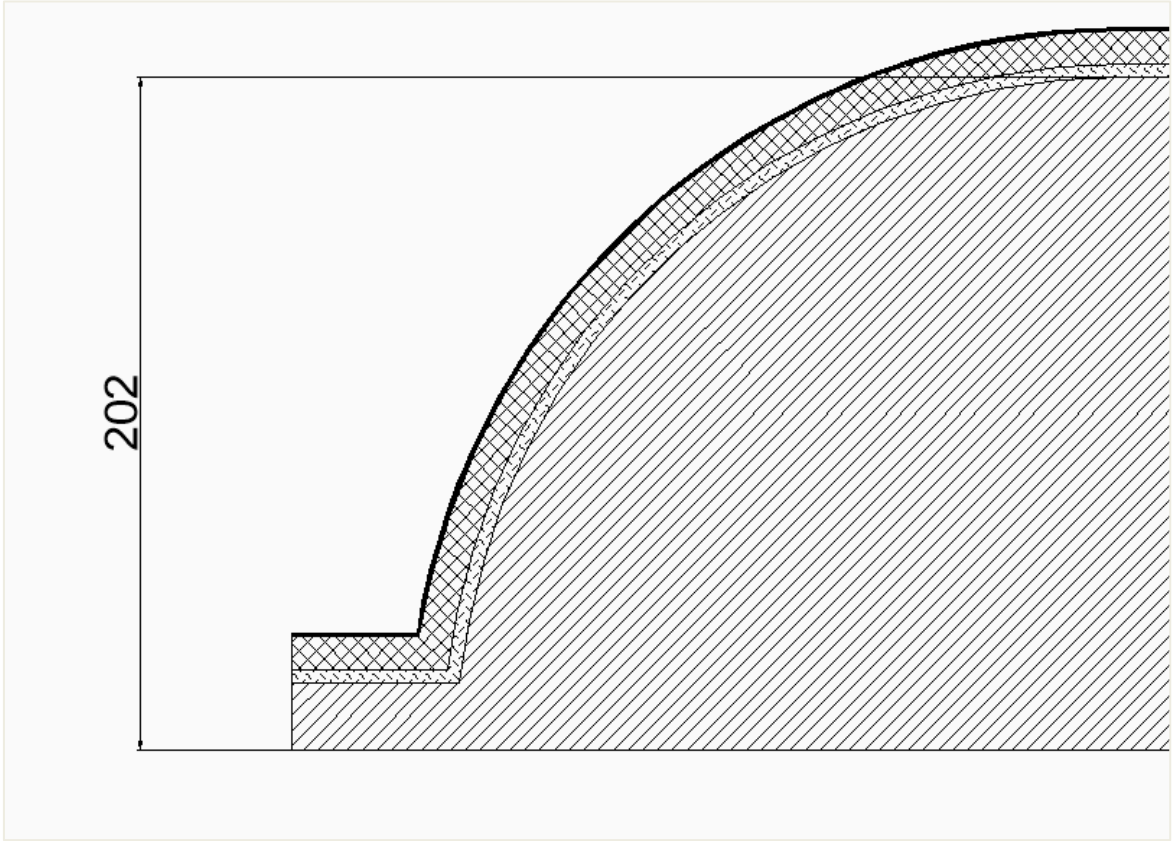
Tank katmanları et kalınlığı ölçüleri (mm)
